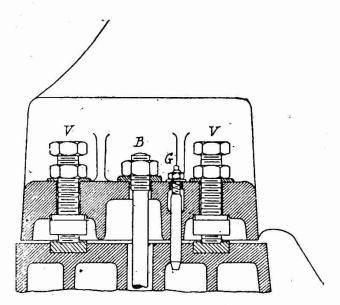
Montage de la carcasse de l'induit sur la plaque de fondation. V, vis permettant de déplacer la carcasse verticalement. G, goupille de centrage.
